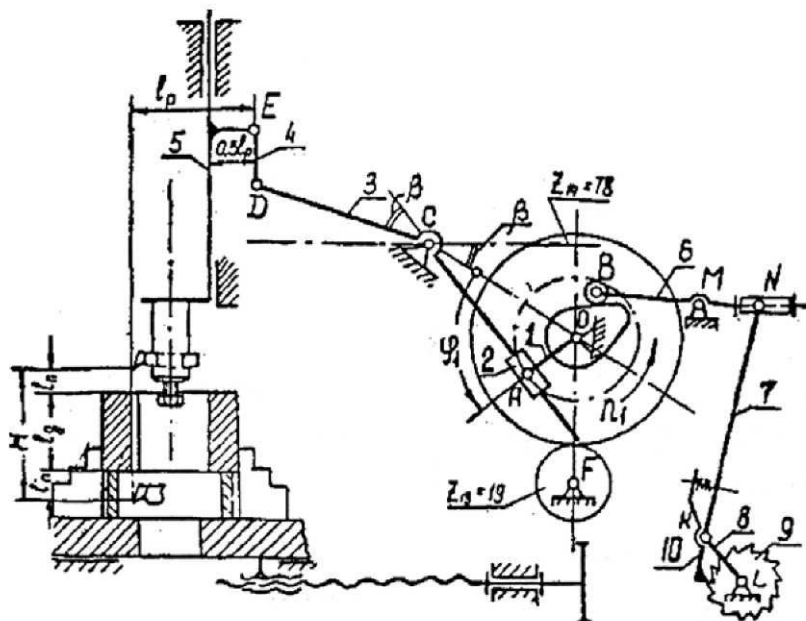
Схема кривошипно-кулисного механизма движения резца и кулачкового механизма подачи стола долбежного станка
